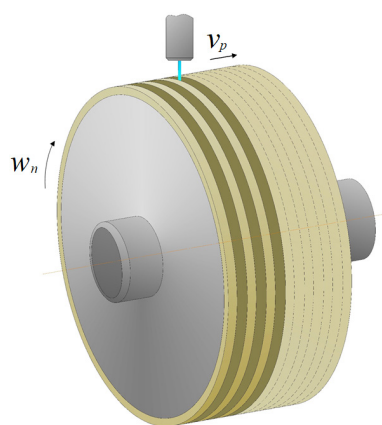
Лазерная резка пакета заготовок дисковых ножей
